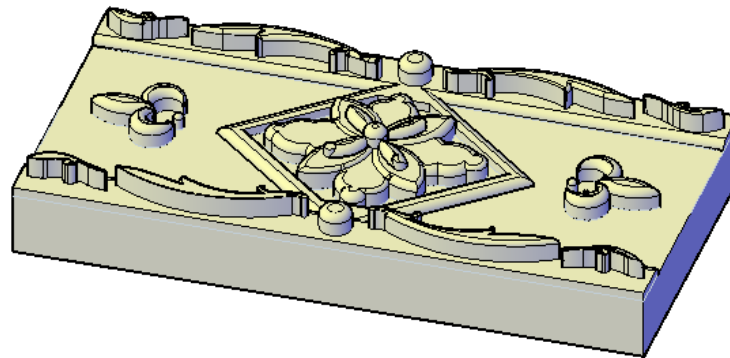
Diseño por computadora 3D de molde 1 para ser fabricado con manufactura aditiva.
